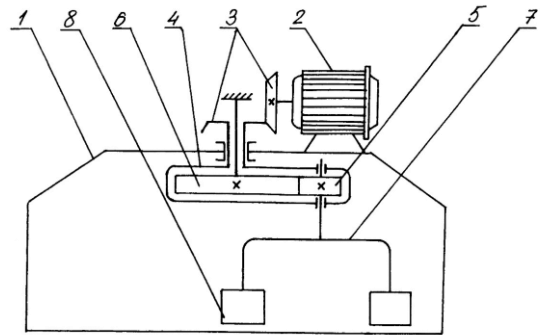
Конструкція роторно-планетарного змішувача з неплоскими лопатями: 1 – корпус; 2 – двигун; 3 – конічна передача; 4 – поворотна траверса; 5 – зубчаста шестерня; 6 – зубчасте колесо; 7 – кронштейн; 8 – змішувальні лопаті
